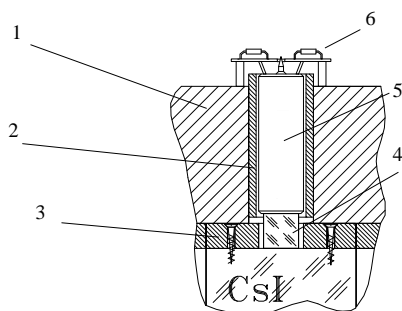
Схема крепления счётчика в октанте. 1 — алюминиевая плита; 2 — магнитный экран; 3 — стальная пластина; 4 — стеклянный световод; 5 — фотоумножитель ФЭУ-60; 6 — делитель напряжения.
